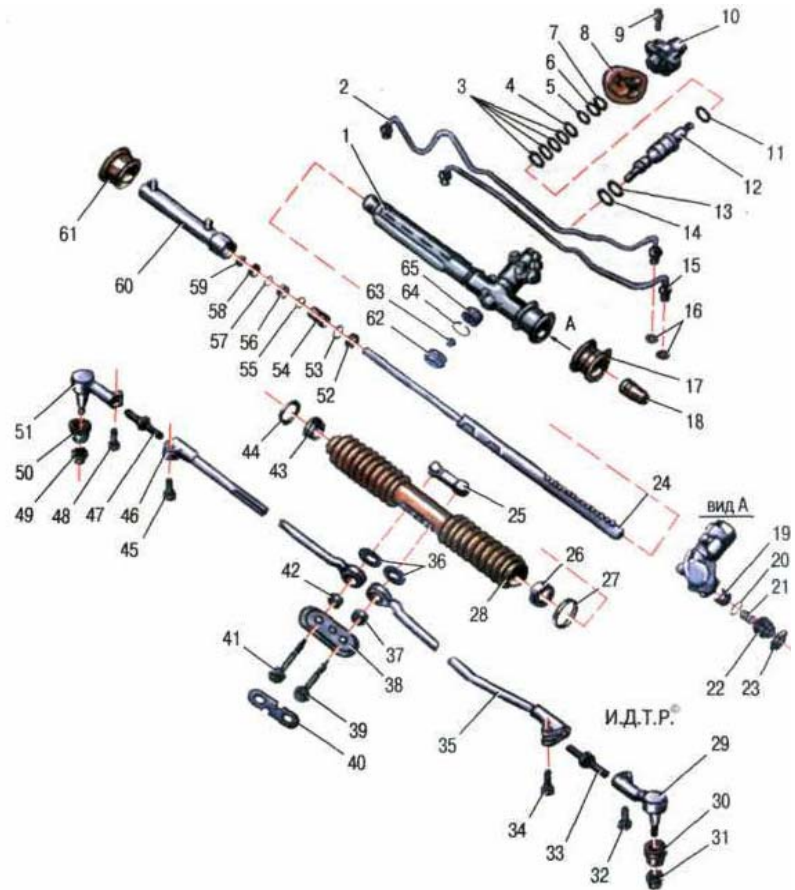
Рулевой механизм с гидроусилителем: 1 - картер рулевого механизма; 2, 15 - трубопроводы; 3, 16, 20, 55, 57, 58 - уплотнительные кольца; 4 - пружинное кольцо; 5 - внутреннее уплотнение вала-шестерни; 6 - пыльник вала-шестерни; 7, 11 - стопорные кольца; 8 - уплотнительный чехол; 9 - стяжной болт; 10 - муфта; 12 - распределитель в сборе; 13 - уплотнение вала-шестерни; 14 - верхняя втулка вала-шестерни; 17, 61 - монтажные втулки; 18 - верхняя заглушка картера; 19 - плунжер; 21 - пружина; 22 - регулировочная пробка; 23 - контргайка; 24 - рейка; 25 - направляющая планка; 26, 43 - втулки кожуха; 27, 44 - хомуты кожуха; 28 - кожух картера; 29 - наконечник рулевой тяги (левый); 30, 50 - чехлы; 31, 49, 59, 63 - гайки; 32, 34, 39, 41, 45, 48 - болты; 33, 47 - регулировочные болты; 35 - левая рулевая тяга; 36, 52 - шайбы; 37, 42 - втулки шарниров рулевых тяг; 38 - опорная пластина; 40 - стопорная пластина; 46 - правая рулевая тяга; 51 - наконечник рулевой тяги (правый); 53 - уплотнение штока; 54 - направляющая втулка; 56 - поршень; 60 - цилиндр; 62 - крышка; 64 - пружинное кольцо; 65 - подшипник
